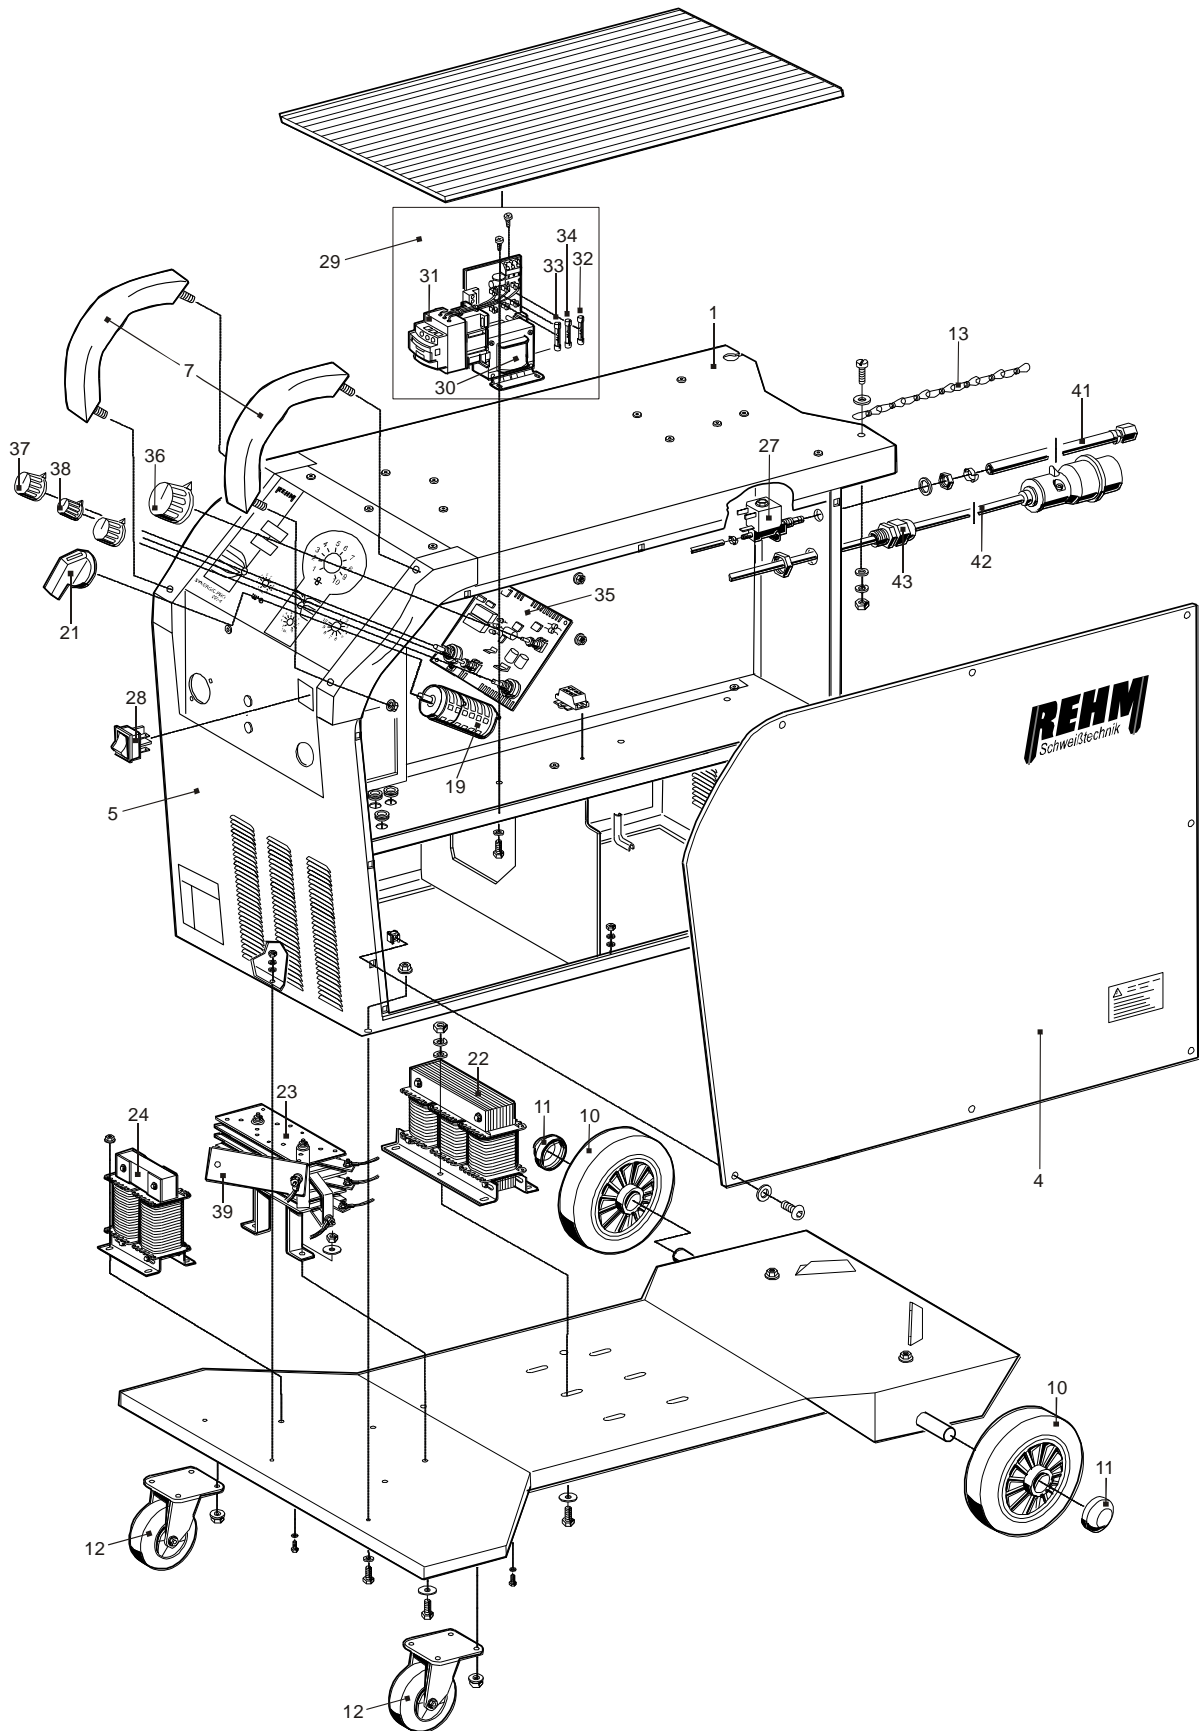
Explosionszeichnung SYNERGIC.PRO² 250-4 – 450-4W (rechts)
